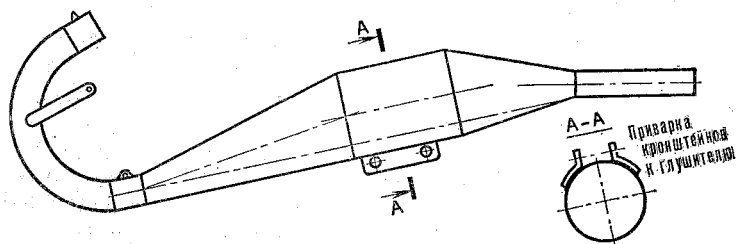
Подгонка формы глушителя по раме мотоцикла
